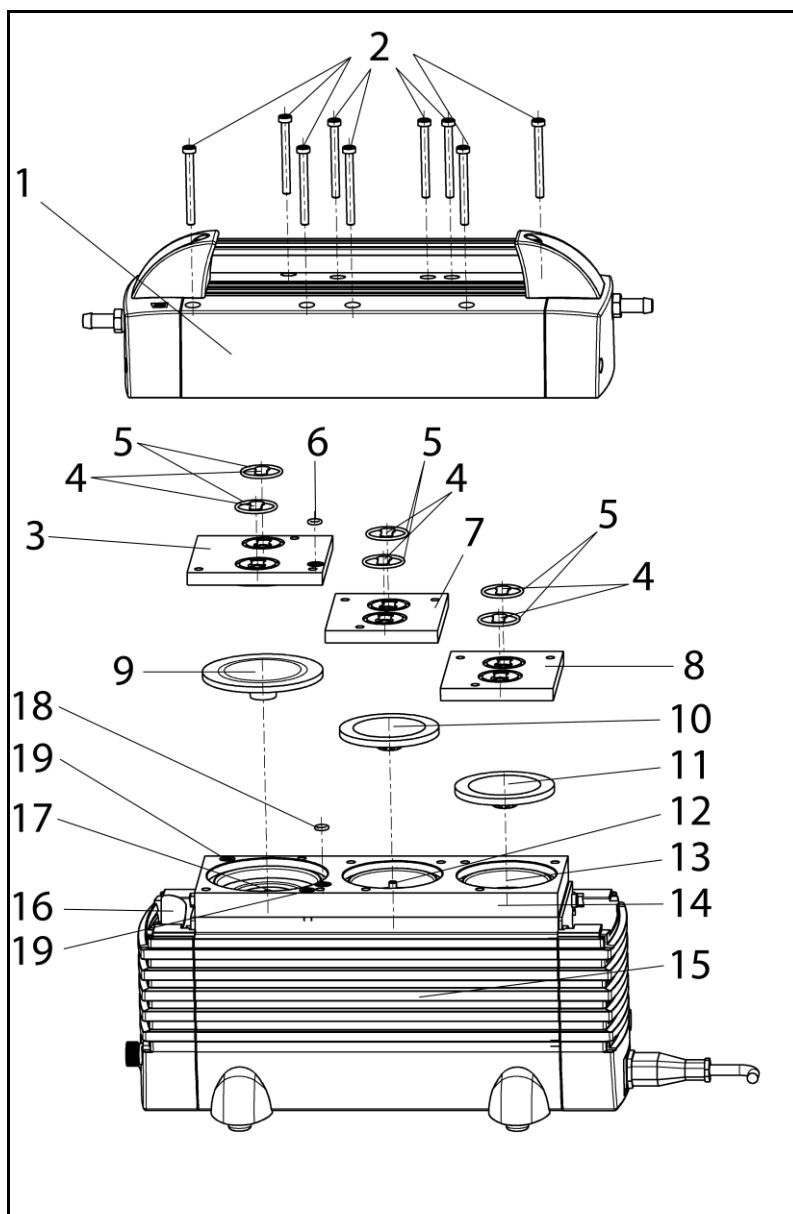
Explosionszeichnung N 920 AP.18 / N 920 AP.29.18
